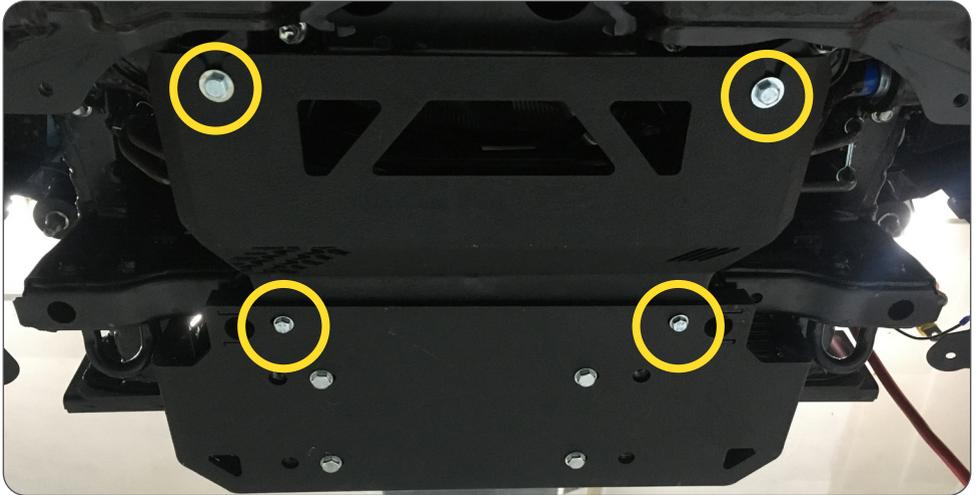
Befestigung Unterfahrschutz / mounting skid plate
